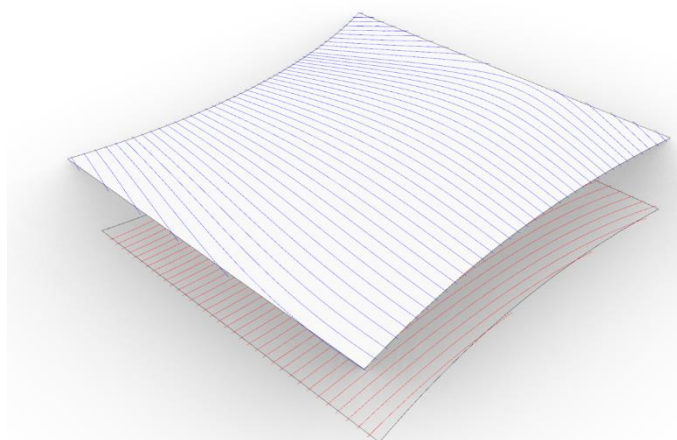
Explosionszeichnung der additiv gefertigten Scheibe mit Extrusionspfaden entlang der Hauptspannungsrichtung (rot, blau)
